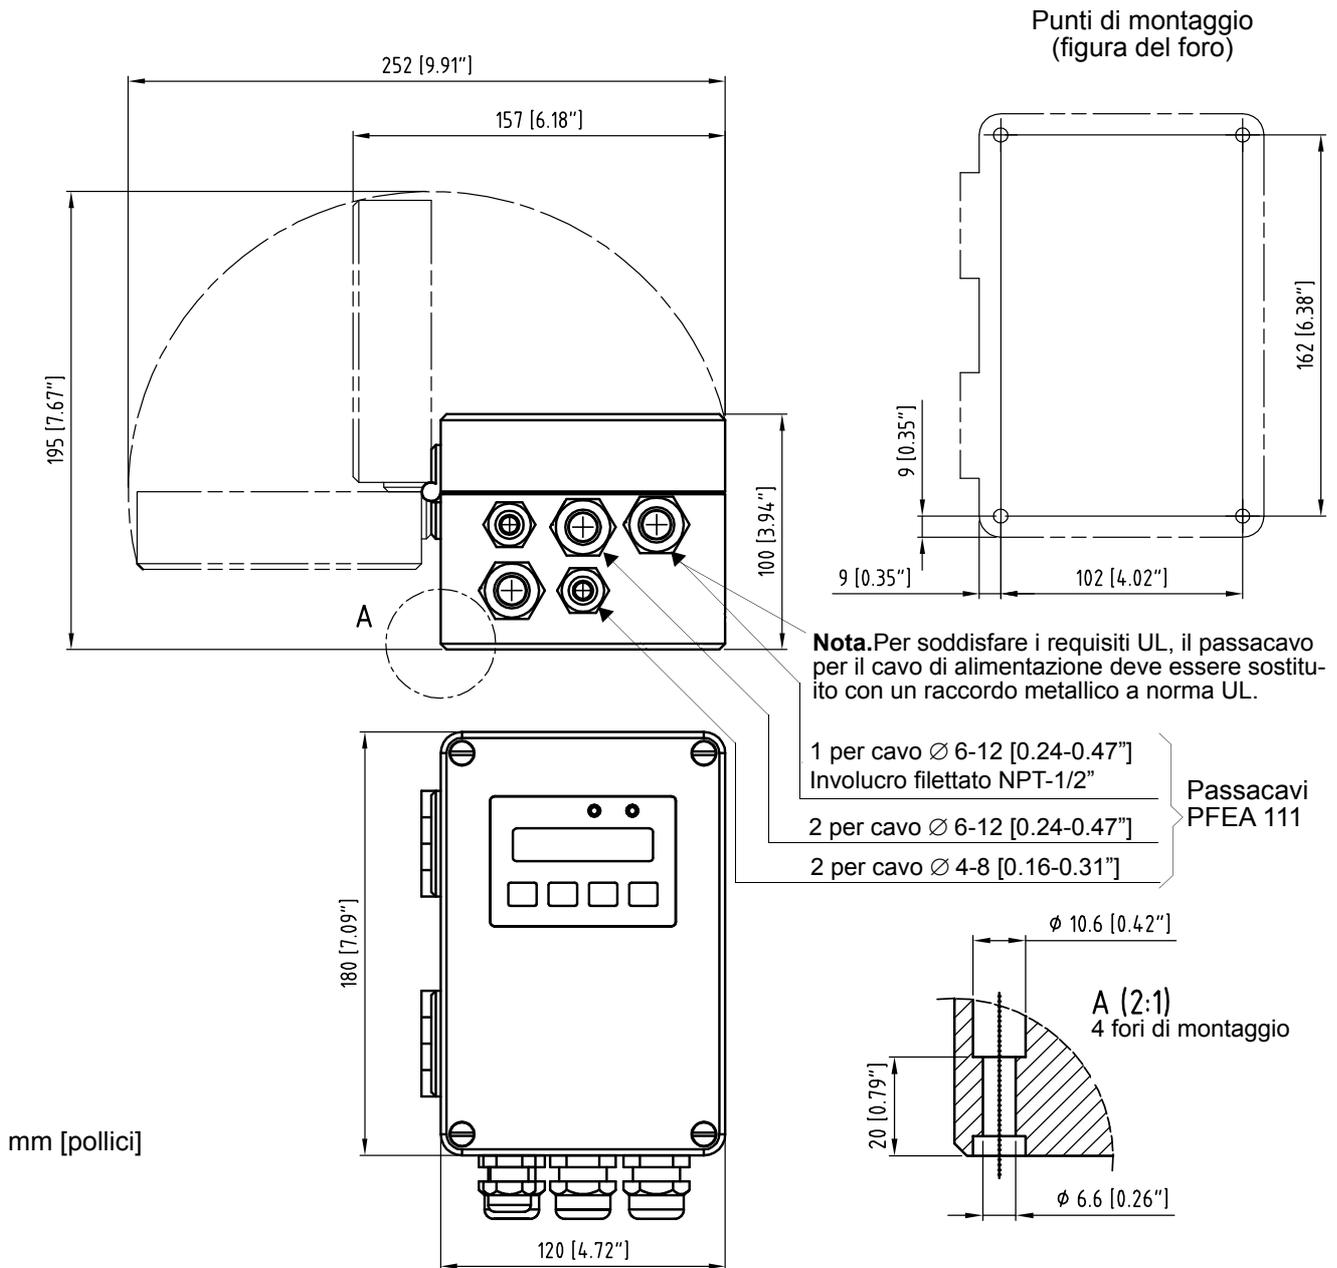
Dimensioni di ingombro per PFEA 111/112
